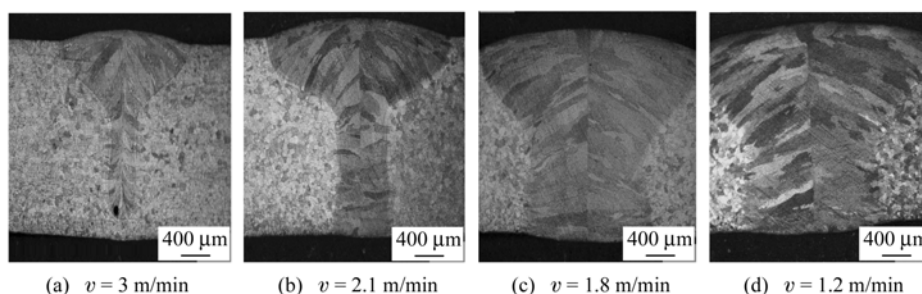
焊接速度对焊缝横截面形貌的影响
